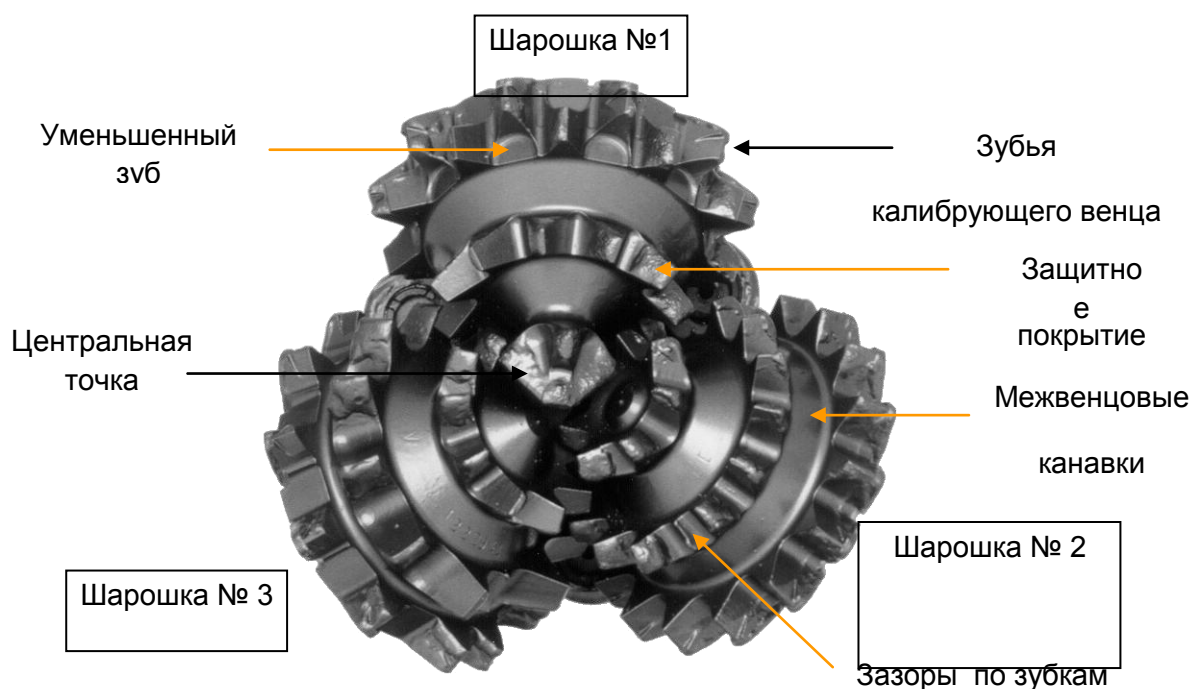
Номенклатура деталей долота с фрезерованными зубьями
